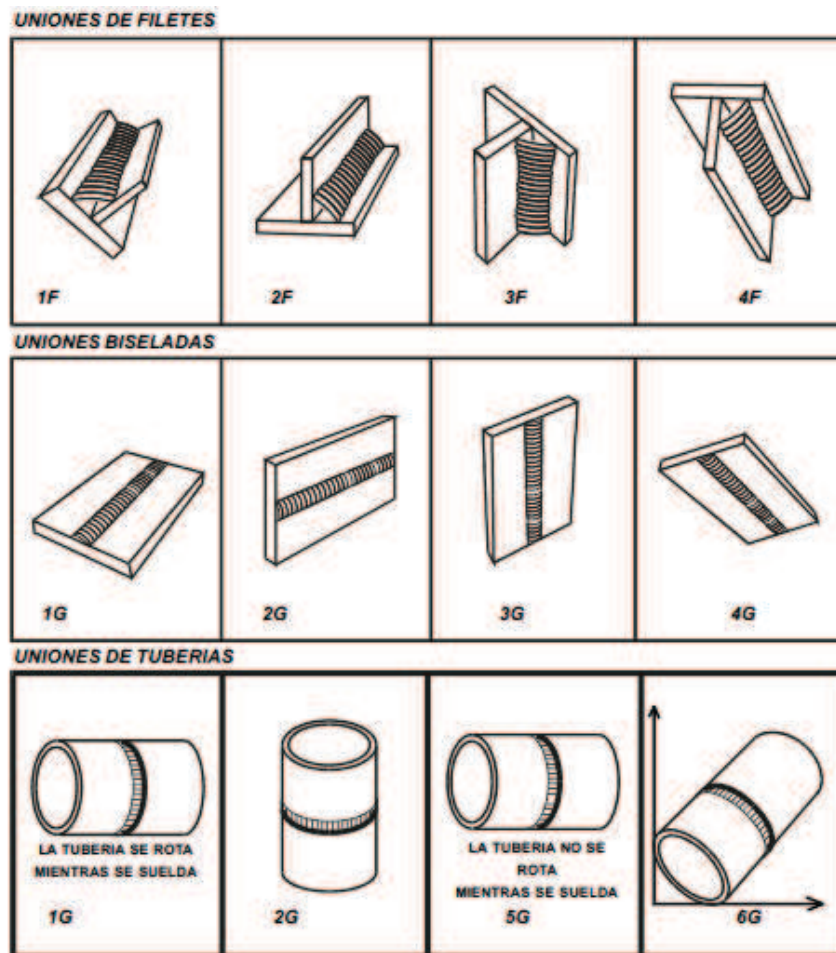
Posiciones de soldadura tipo filete, ranura y para tubos
